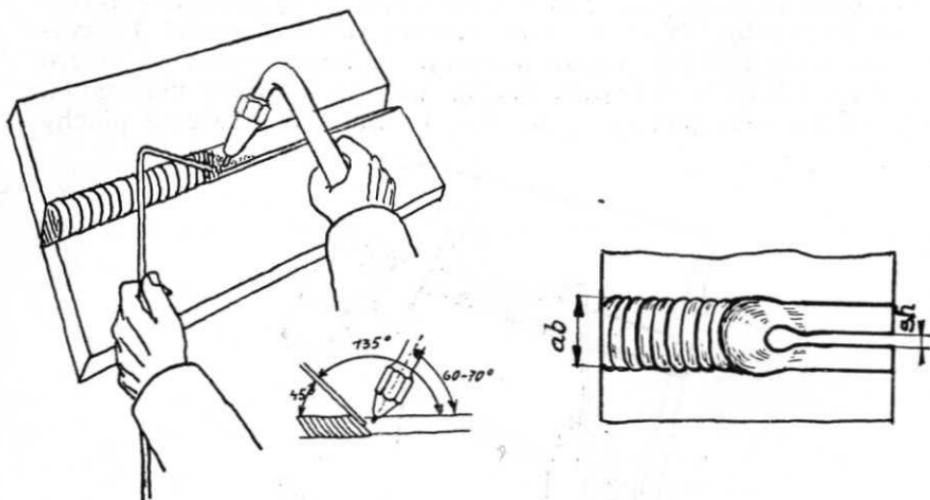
Držení hořáku a vedení drátu při sváření levosměrném (doleva). Drát se pohybuje stejnomořně ve směru svaru. Aby byl natavený materiál po celé spáře dobře rozdělen, pohybuje svařec hořákem přes šev.
